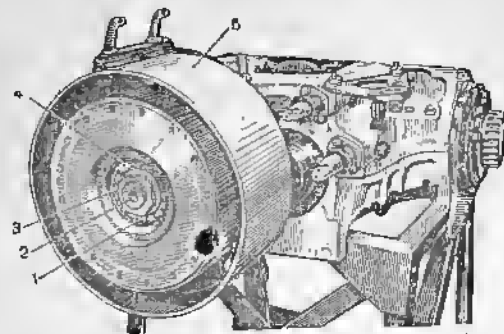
Бортовой фрикцион, установленный на конце главного вала четырехскоростной коробки передач:
